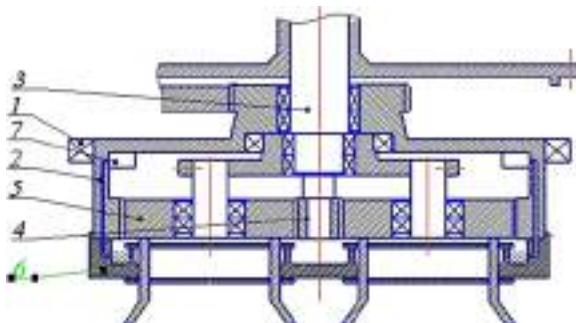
Конструктивная проработка: 1 – подшипник; 2 – корончатое колесо; 3 – вал; 4 – неподвижная шестерня; 5 – сателлит; 6 – крышка; 7 – насос
